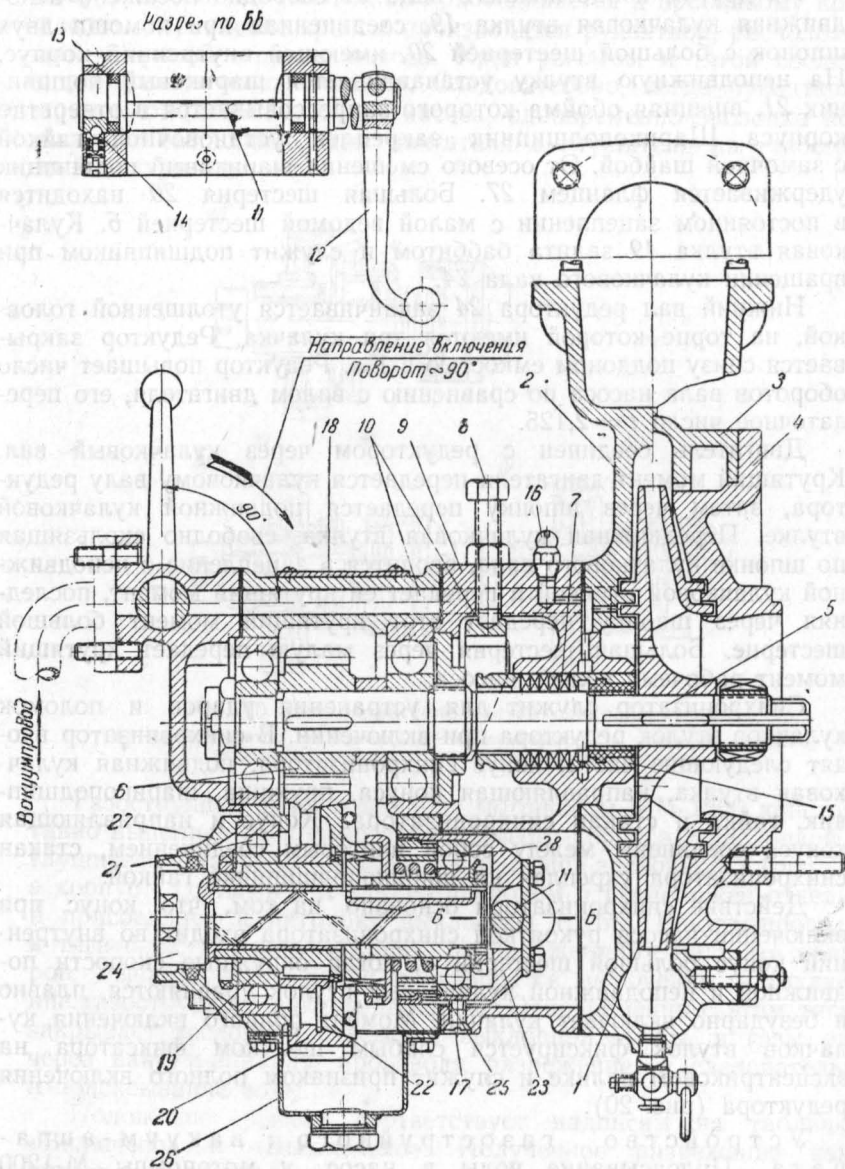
Центробежный насос ПН-1200 (продольный разрез):
